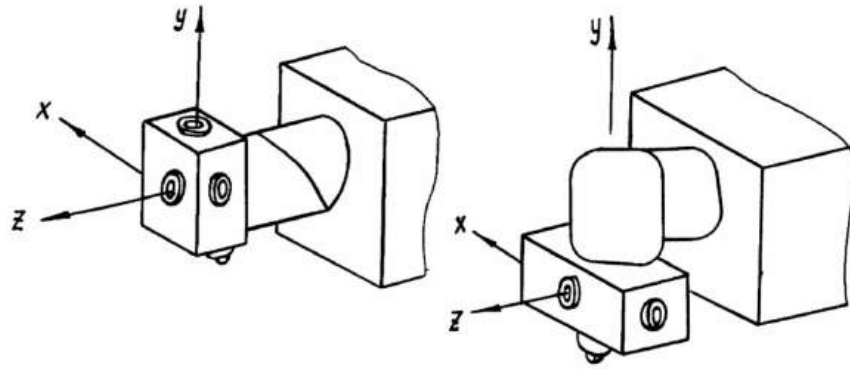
Поворотна трьохкоординатна насадка револьверної головки
